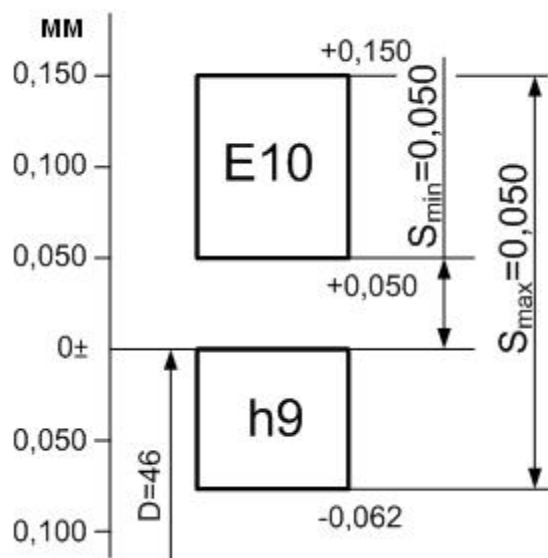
Схема полів допусків деталей з'єднання  $\varnothing 46E10/h9$
